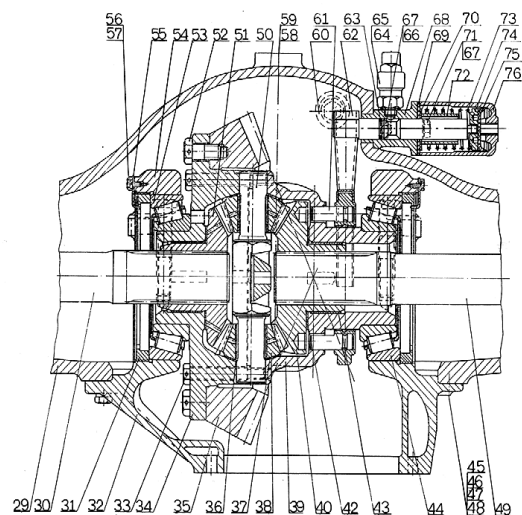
Двойная центральная главная передача со смещением ведомой цилиндрической шестерни вниз:
